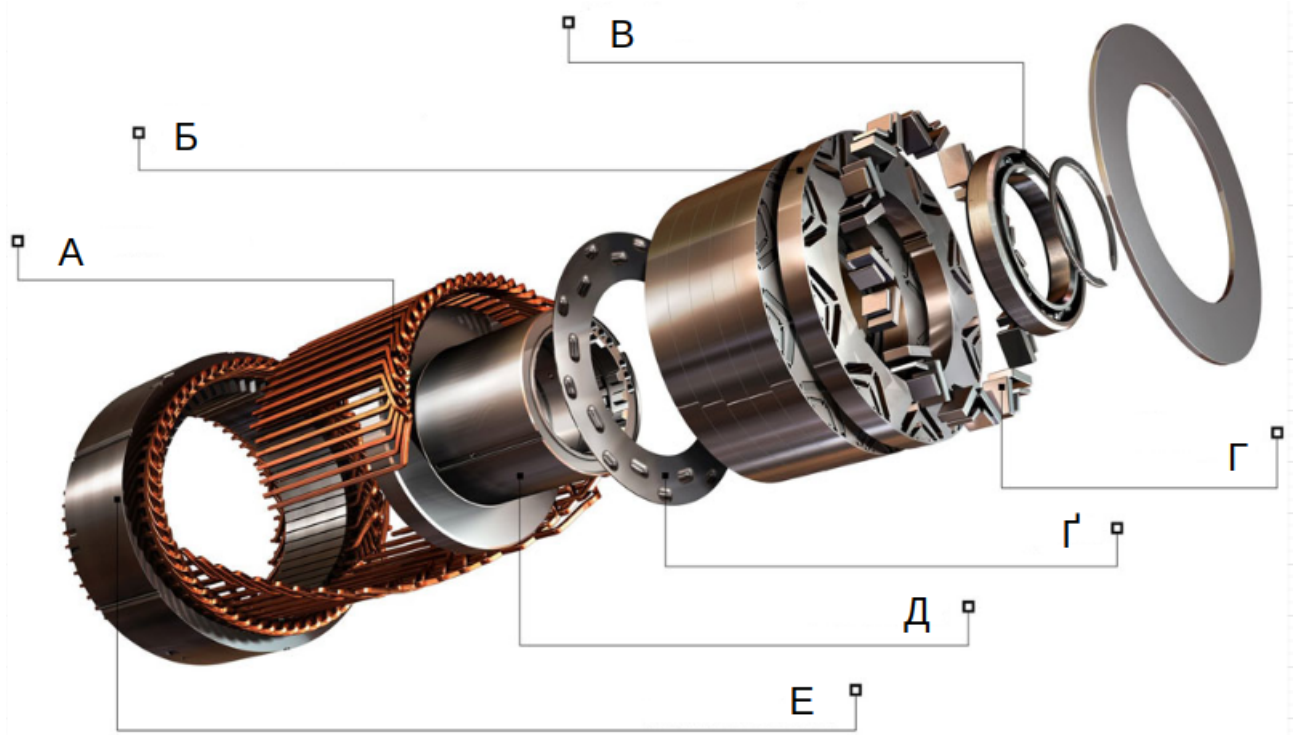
Загальна конструкція двигуна PMSM: А - прутковий дріт; Б - ротор із ламінованої сталі; В - вузол опорного підшипника; Г - магніти; Г' - стальна плита; Д - хаб ротору; Е - статор із ламінованої сталі;
